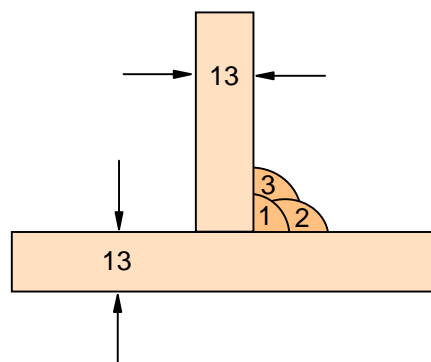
Sequência de deposição de passes na soldagem de uma junta em T
